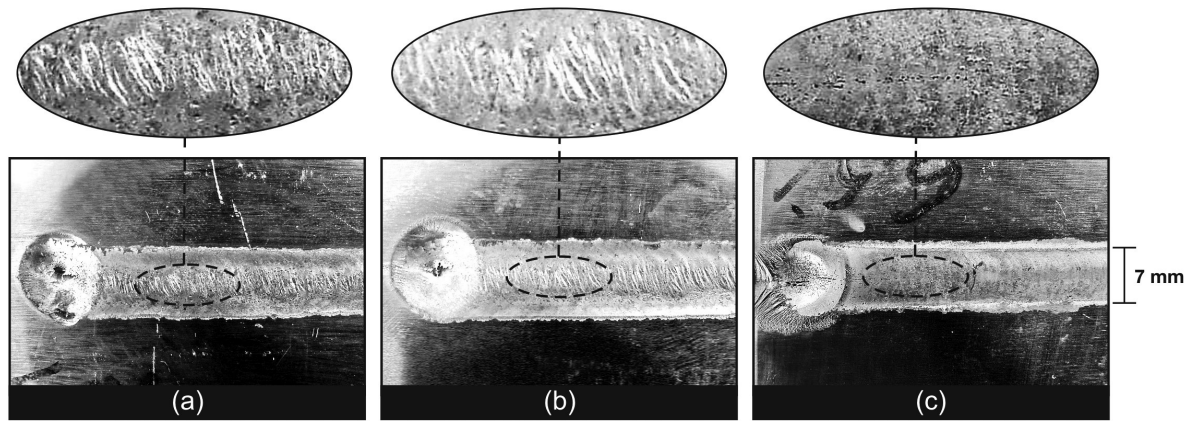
(a) Cordão de solda realizado com % EP = 5,0% ; (b) Cordão de solda realizado com % EP = 6,0% ; (c) Cordão de solda realizado com % EP = 6,5% e considerado de aparência aceitável. Cordões de solda realizados com velocidade de soldagem de 3,33 mm/s (20 cm/min), corrente de soldagem regulada em 100 A para ambas as polaridades e período de 20 ms
